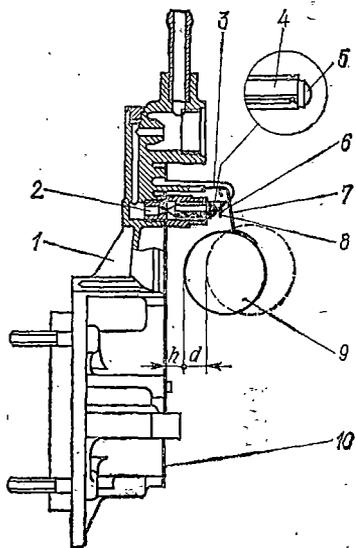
Установка уровня топлива в поплавковой камере:
